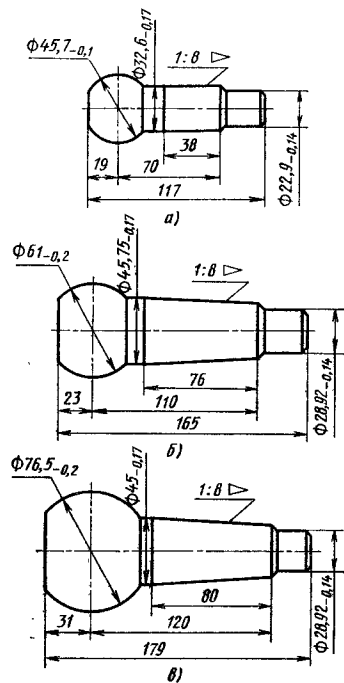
Заготовки шаровых пальцев грузовых автомобилей
